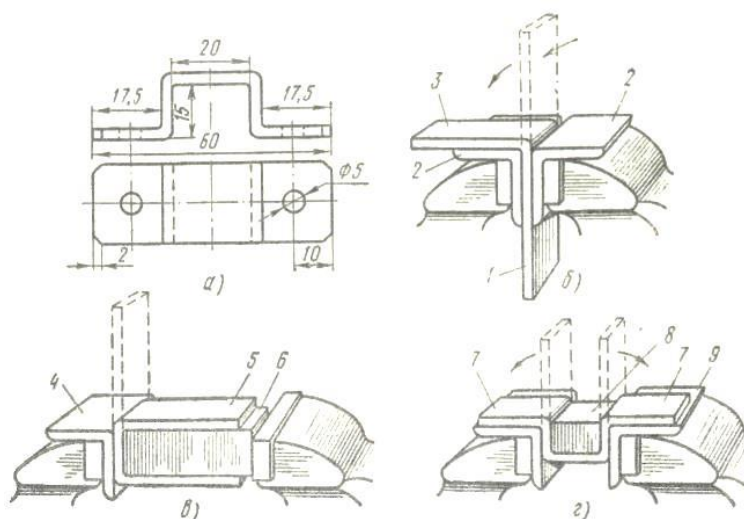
Гибка прямоугольной скобы: *а* — определение длины заготовки, *б* — гибка одного конца, *в* — гибка второго конца, *г* — формирование скобы; 1 — заготовка, 2 — нагубники, 3, 5 — концы скобы, 4, 9 — угольники, 6 — большой брусok-оправка, 7 — лапки, 8 — меньший брусok-оправка
